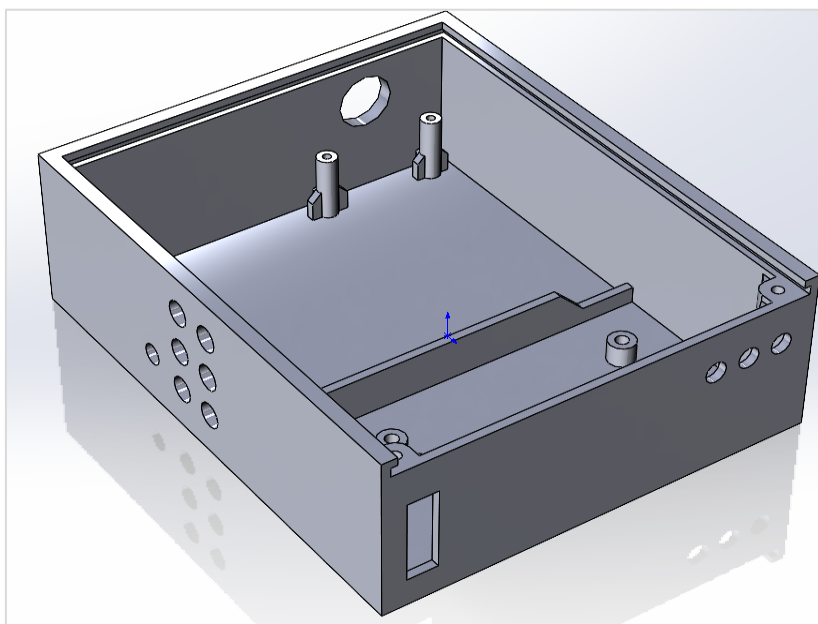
Общий вид нового корпуса, часть 1
